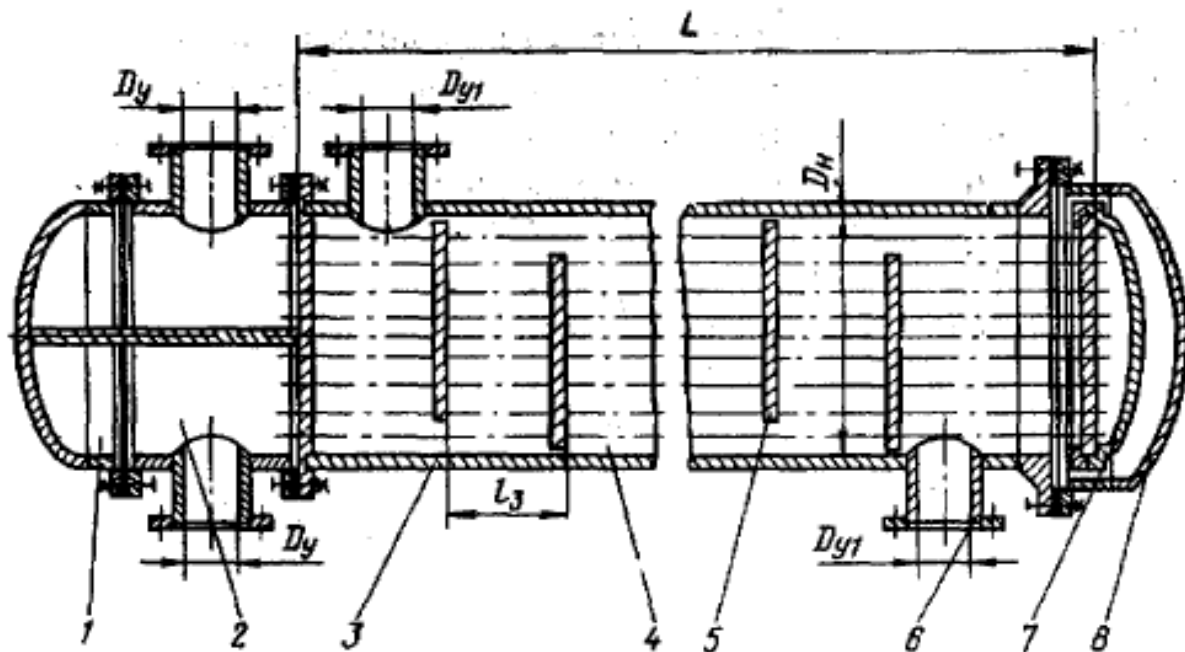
Кожухотрубчатый теплообменный агрегат с плавающей головкой
